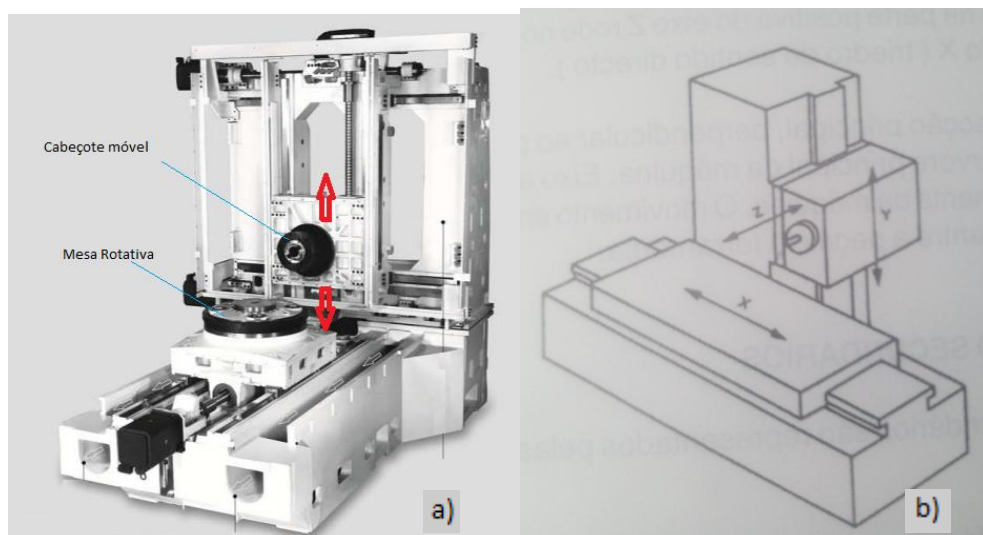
a) HMC -Horizontal Machine Center (extraído de: <http://www.jyoti.co.in>)
